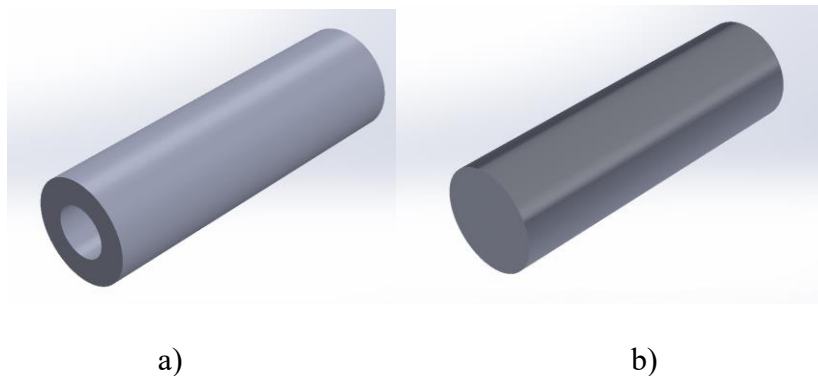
a) Vista isométrica frontal del bocín, b) Vista isométrica posterior del bocín
